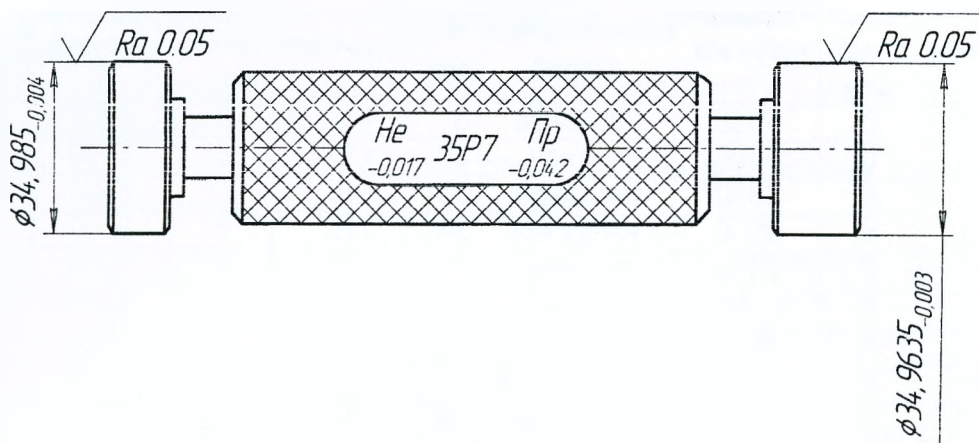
Калибр-пробка для контроля отверстия 35P7
